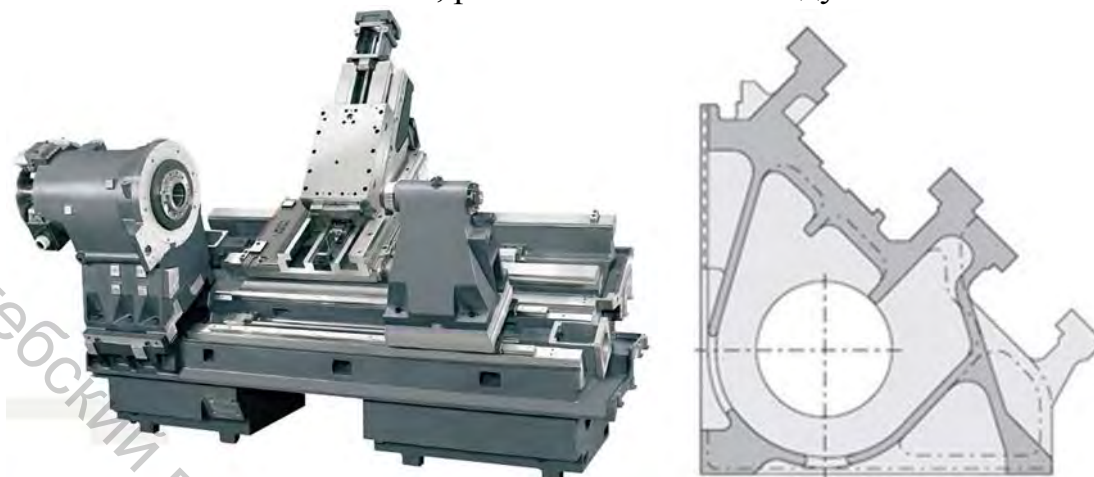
Общий вид токарного станка с ЧПУ NL3000MC/3000 (DMG MORI) и его станина
